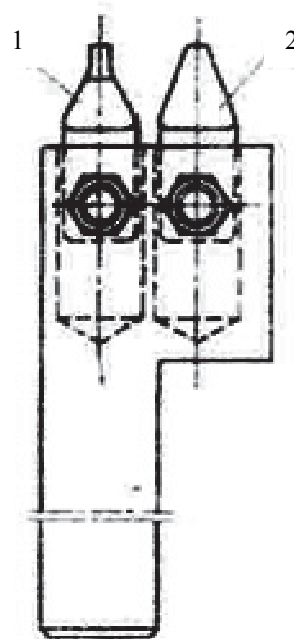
Державка с двумя резцами для нарезания трапецеидальной резьбы
